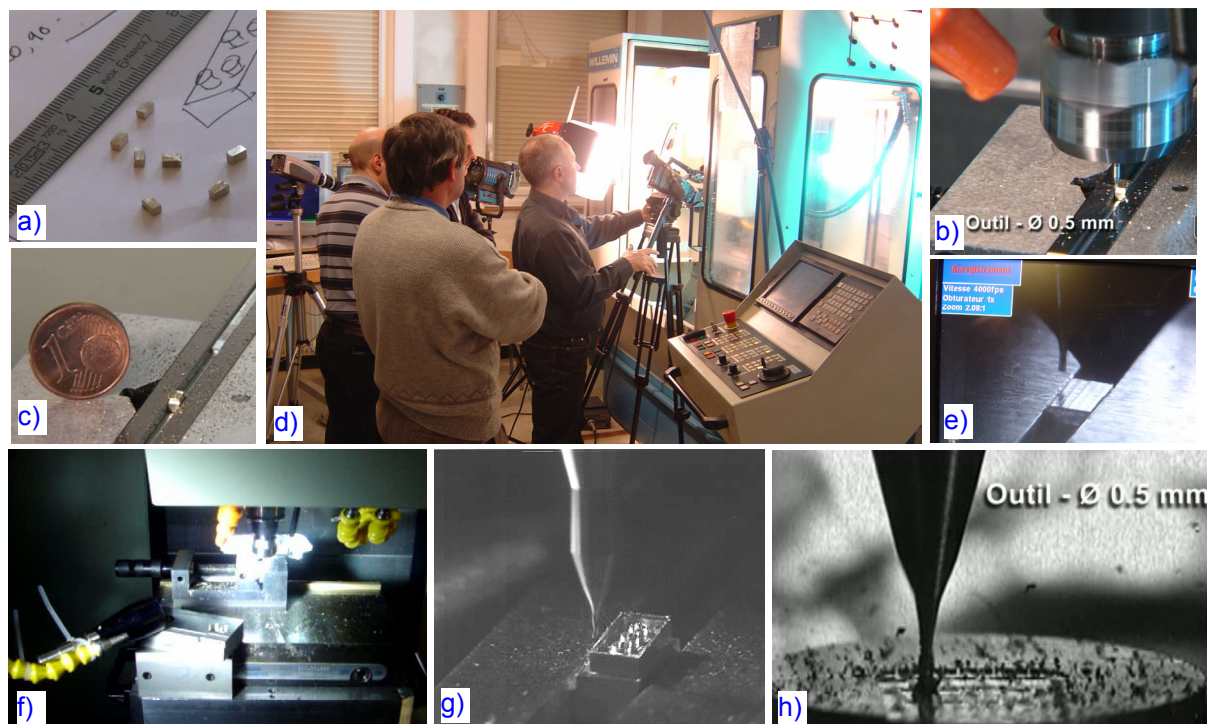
Observation par caméra ultra rapide (4 000 images /s) : a) pièce brute, b) usinage D0.5Z2, c) pièce usinée, d) prise de vue et e) moniteur de contrôle, f, g, h) usinage
